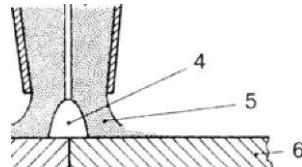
Схема процесса сварки в среде защитного газа:
